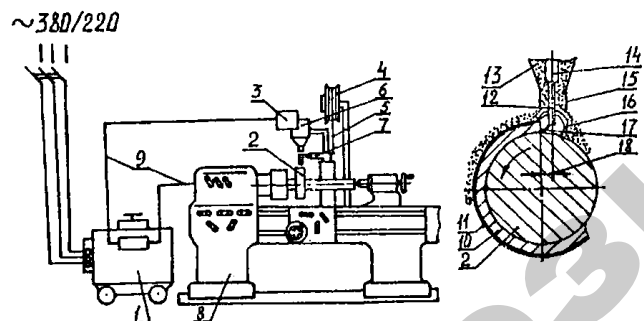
Схема установки для наплавки деталей под флюсом:
